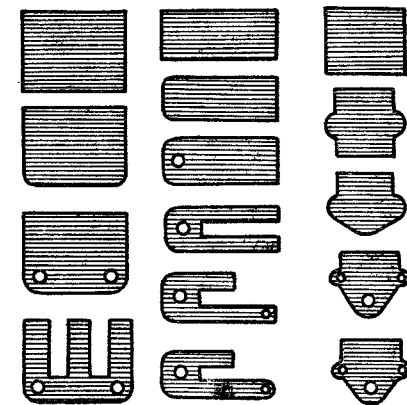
Последовательность штамповки трех деталей по элементам контура
